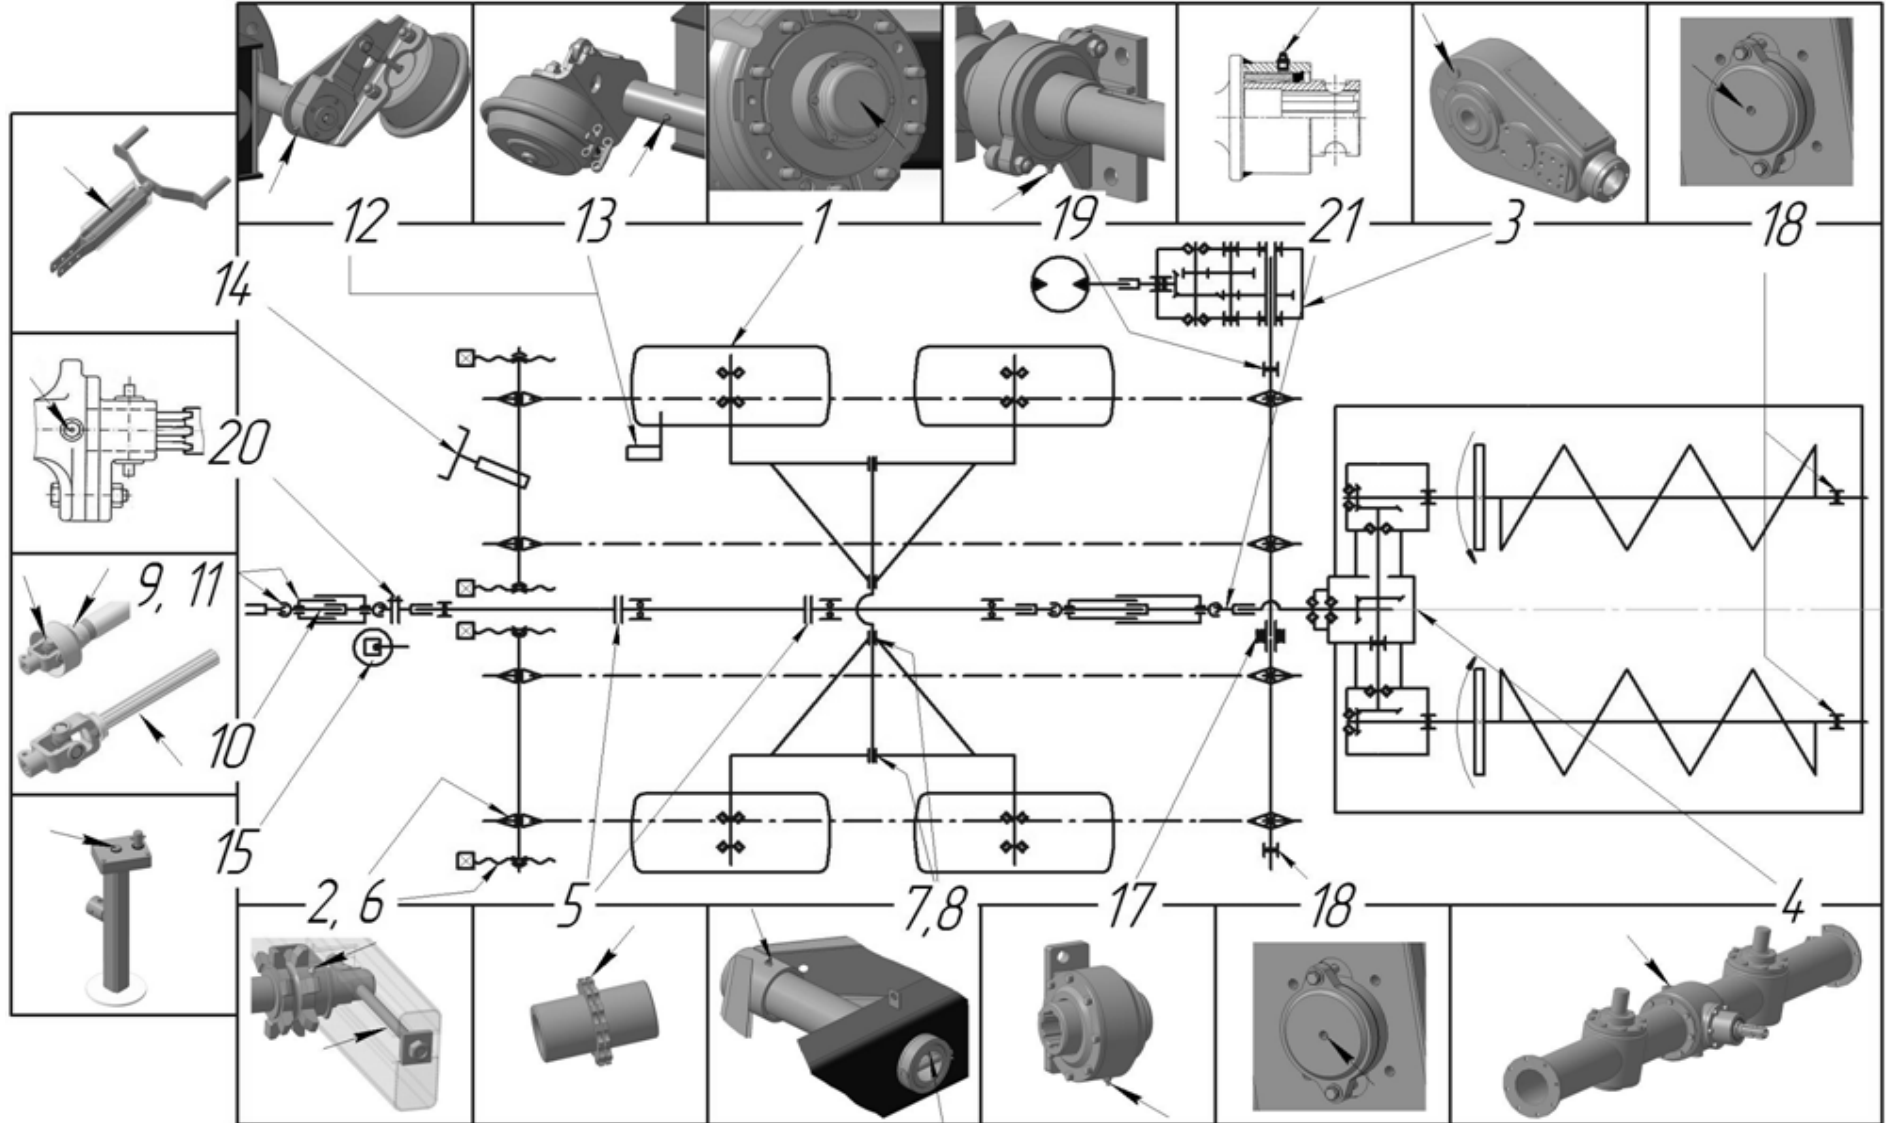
Схема смазки (машина с разбрасывателем с двумя вертикальными барабанами)
